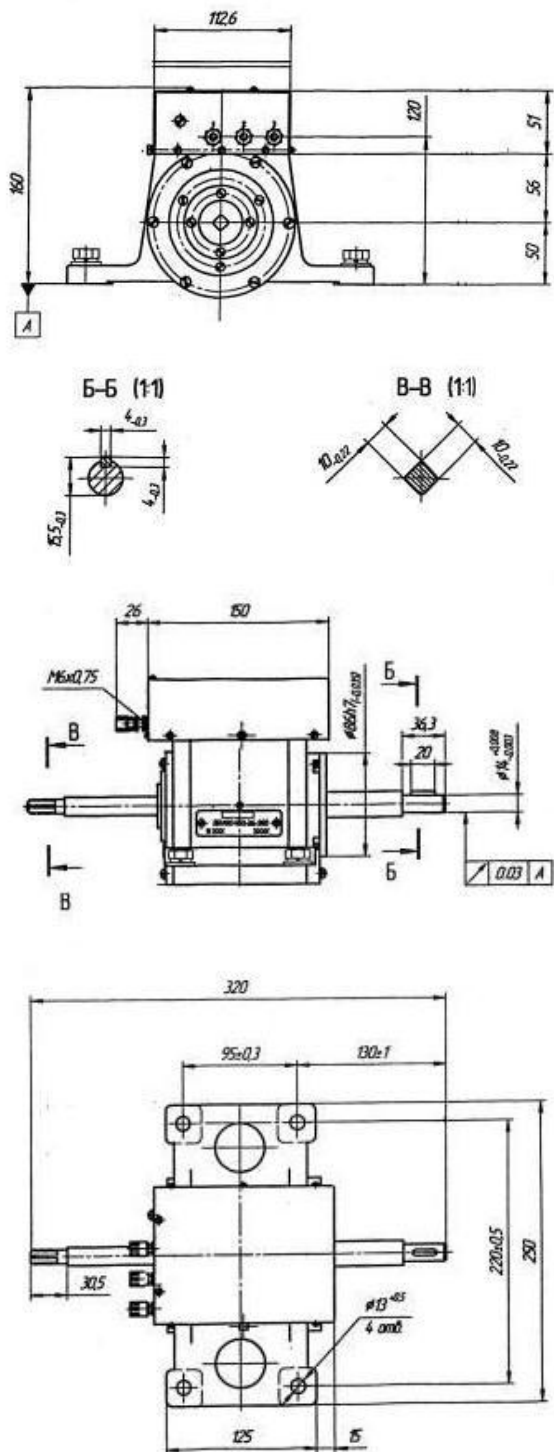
Габаритные и установочно-присоединительные размеры ДБУ
